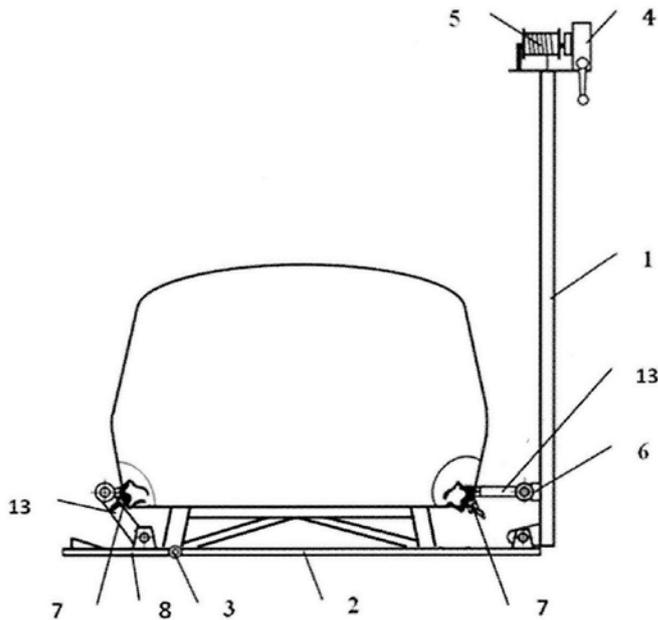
общий вид подъемника с кузовными захватами
